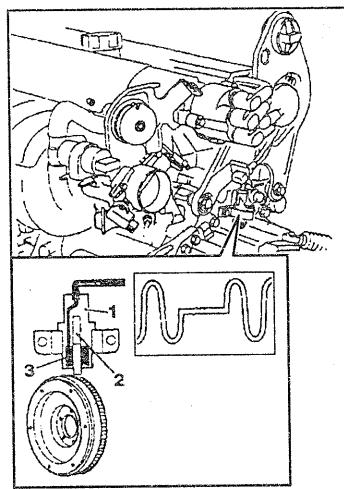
Датчик положения коленвала (1 - корпус; 2 - магнит; 3 - катушка)
